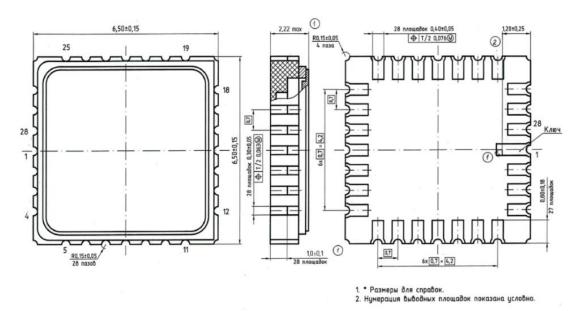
Габаритный чертеж корпуса 5123.28-1.01 (размеры в мм)
